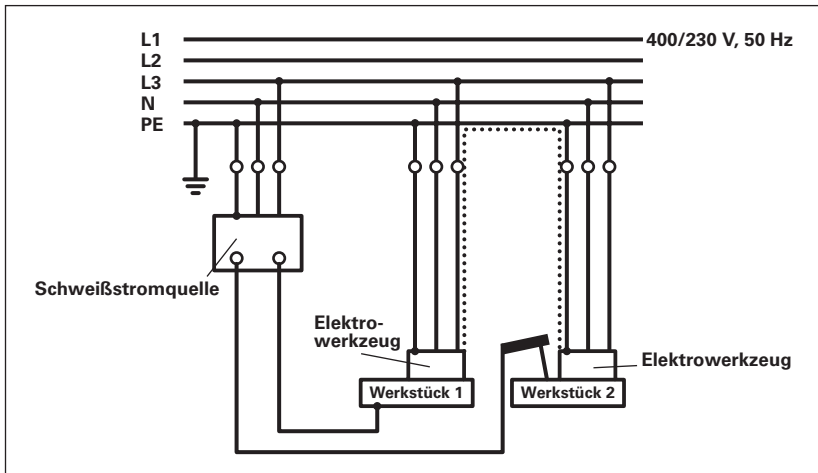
Der Schweißstrom fließt über die Schutzleiter der beiden Elektrowerkzeuge, wenn irrtümlich an Werkstück 2 geschweißt wird, ohne die Schweißstromrückleitung von Werkstück 1 auf Werkstück 2 umzuklemmen.
